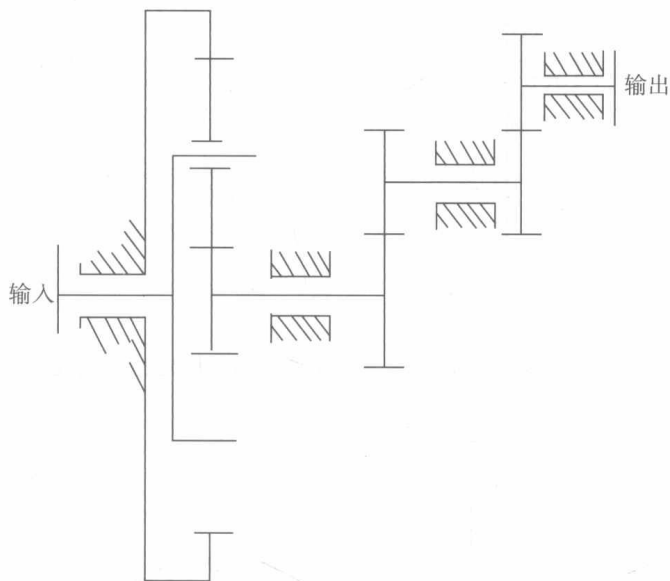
单级行星轮系与二级平行轴结构的行星齿轮增速传动机构简图
